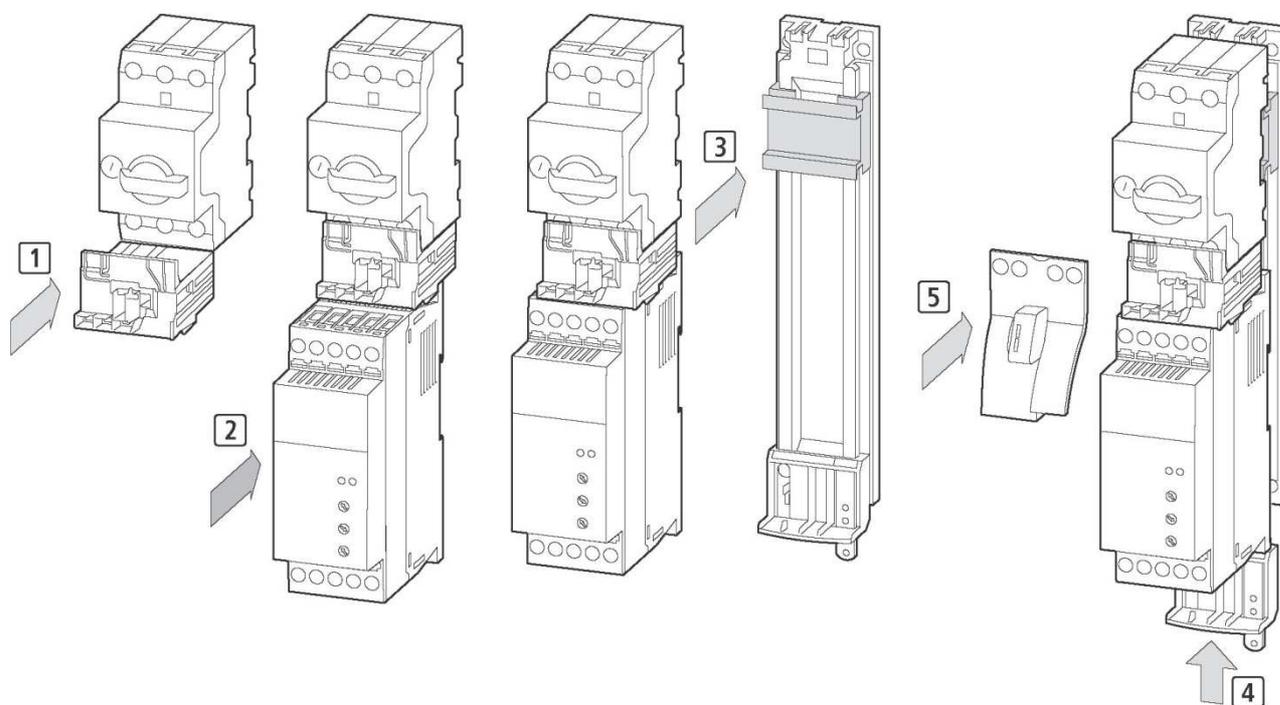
Montaje en carril o adaptador de embarrado para aparatos de hasta 12 A
